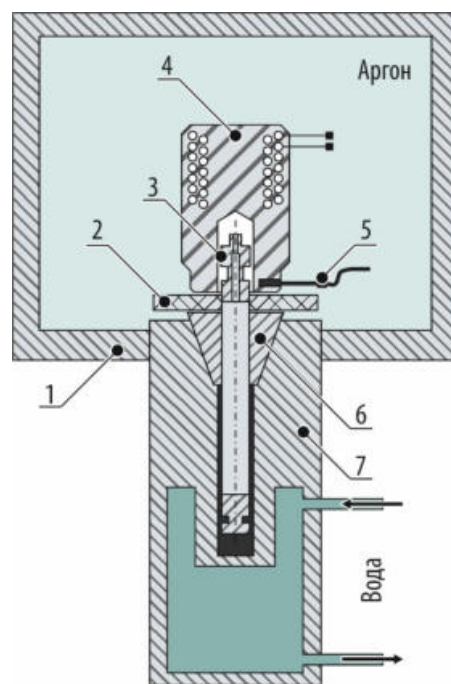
Схема установки для термообработки сварных соединений: 1 — корпус герметичной камеры; 2 — шайба графитовая; 3 — изделие; 4 — нагреватель; 5 — термоэлектрический преобразователь; 6 — цанга медная; 7 — оправка съёмная
